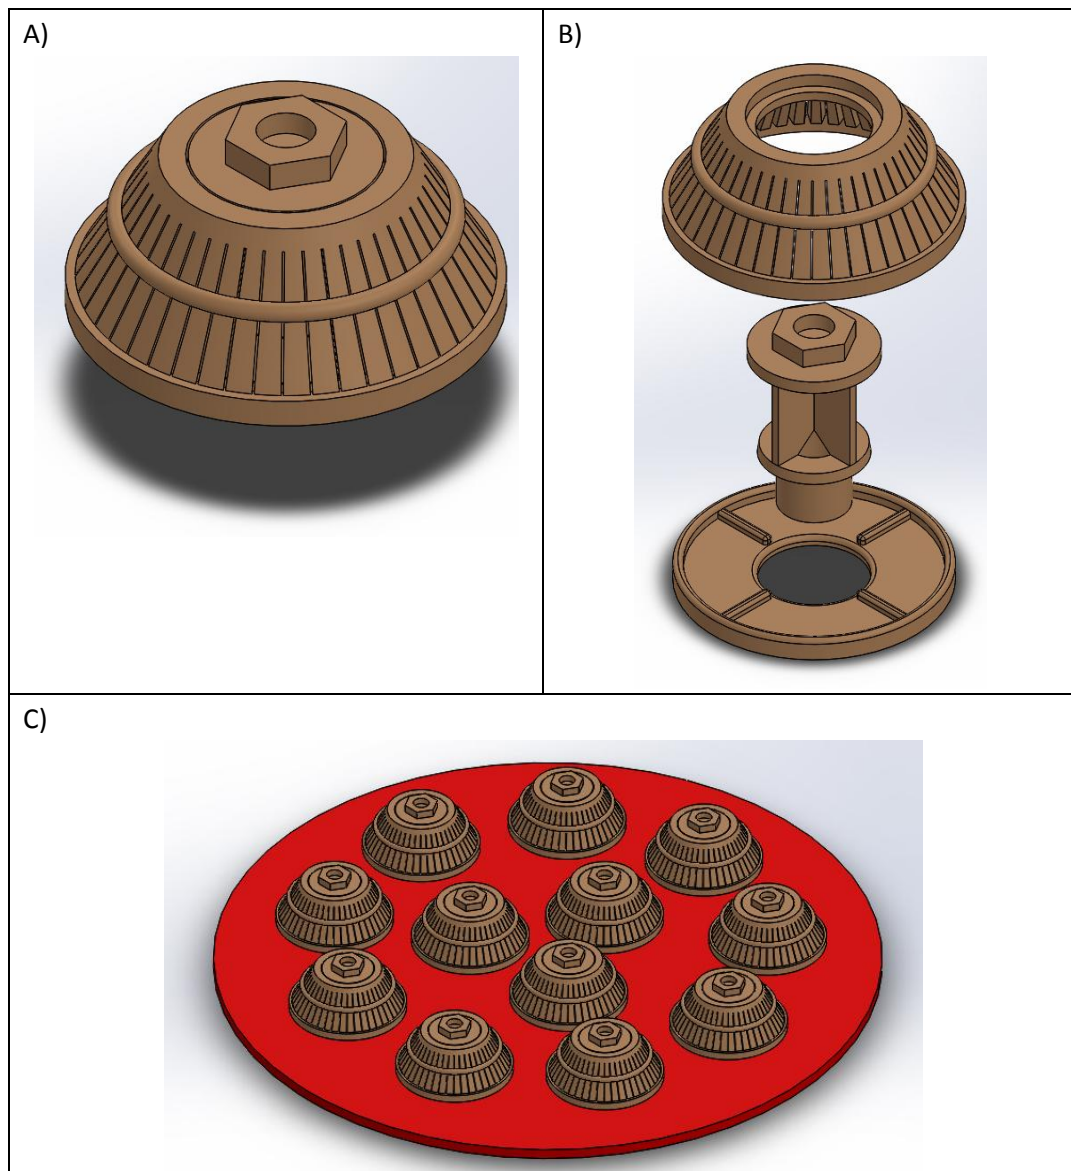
Drenaje formado por crepinas insertadas en placa. A) Crepina montada; B) Crepina, vista explosionada; C) Crepinas instaladas en placa. (Elaboración propia).
